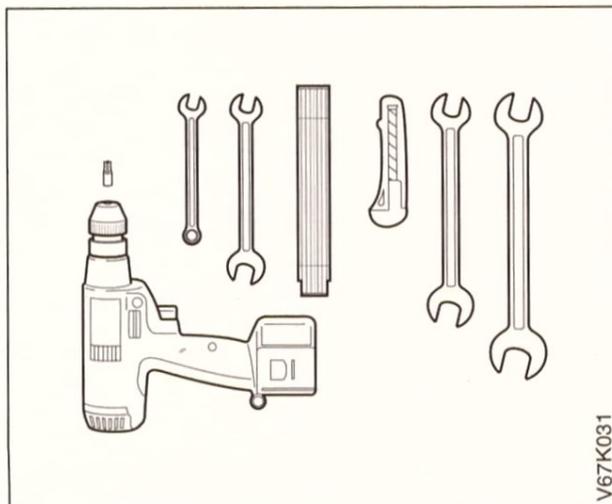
Montage-Werkzeug: Zollstock, Bohrmaschine, Kreuzschlitz-Bit PZ3, Maulschlüssel Nummer 13, 17, 21 und 24.
